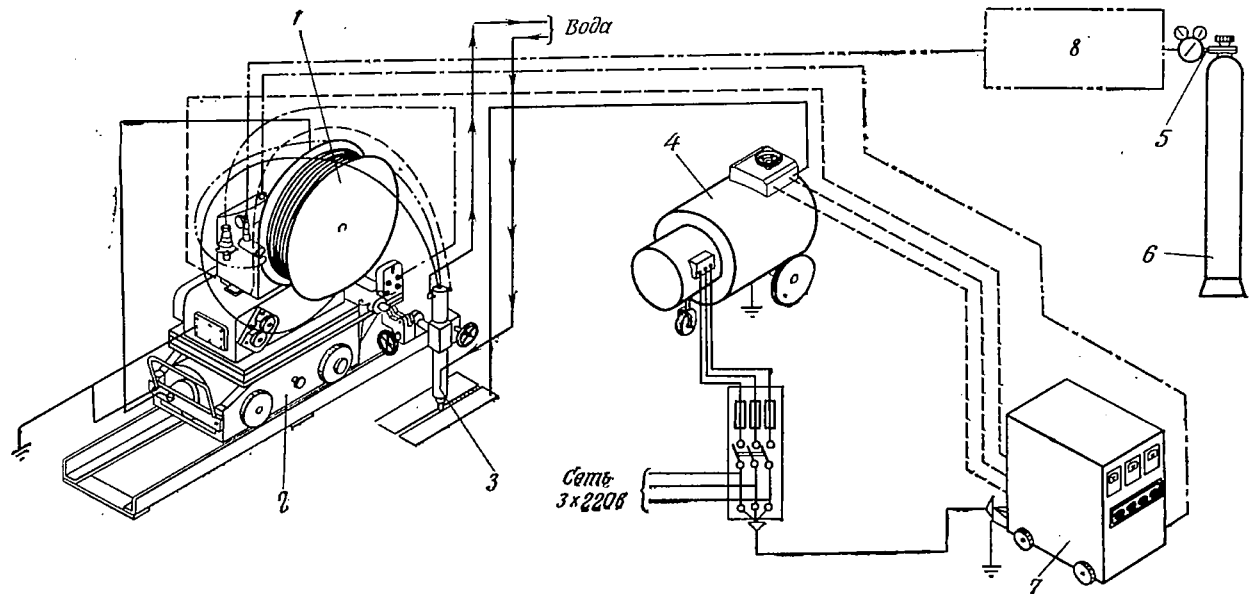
Схема установки ГДУ-2А для сварки плавящимся электродом.
